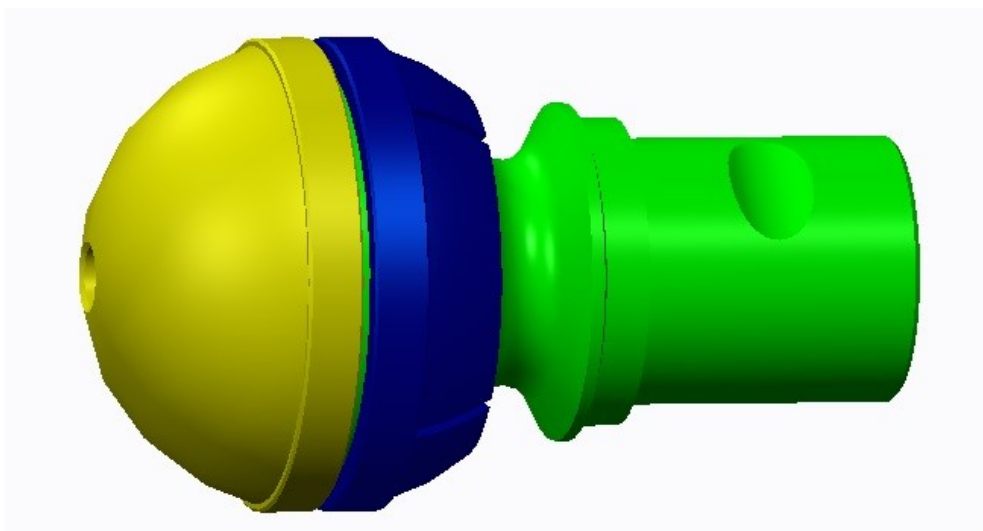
Detail sestavy přední nápravy SOR BN004, kulové čepy jsou zvýrazněny zeleně [1]
